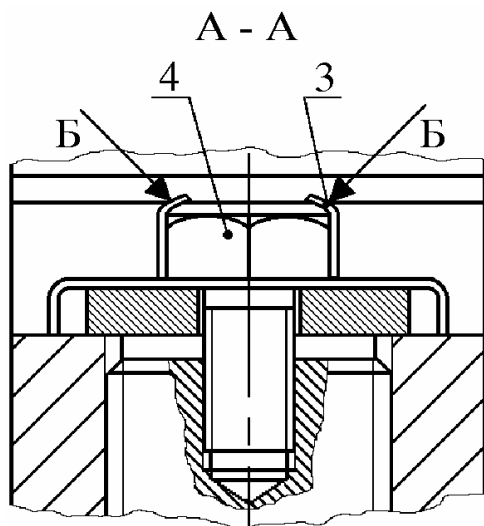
Сборка промежуточного вала с вилкой шлицевой:
